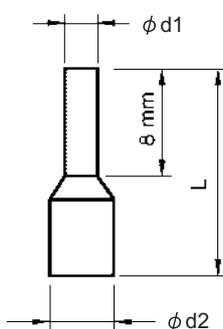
Taille de la borne sans soudure droite
